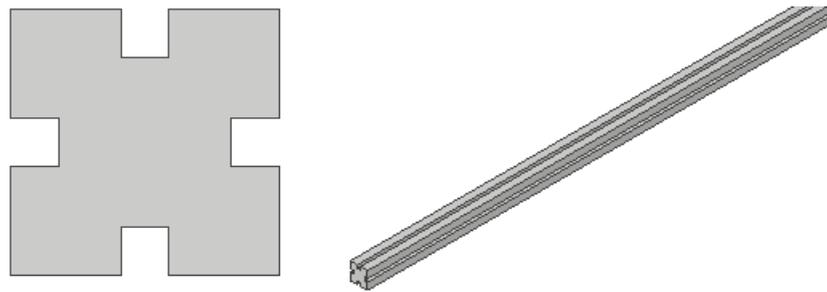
Perfil cuadrado con canales para las vigas de polietileno
